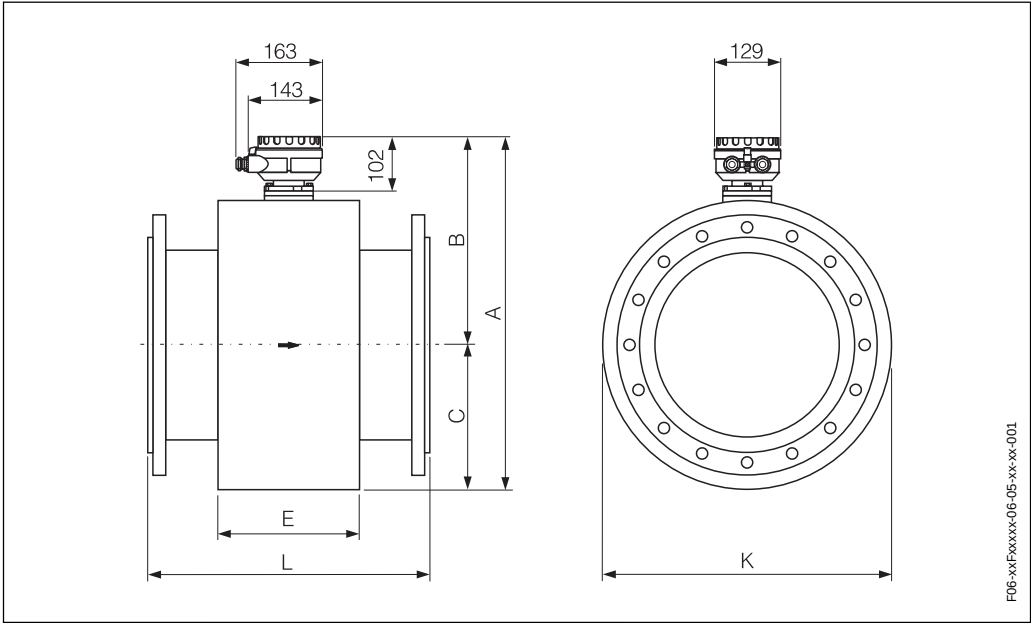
Dimensoes do Promag W / DN ≥ 350 (versao remota)
